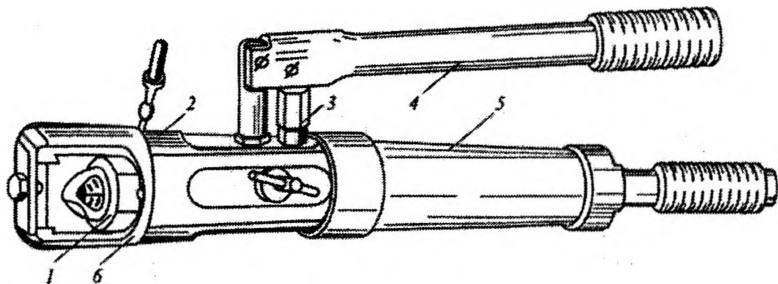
Ручний гідравлічний прес РГП-7:
